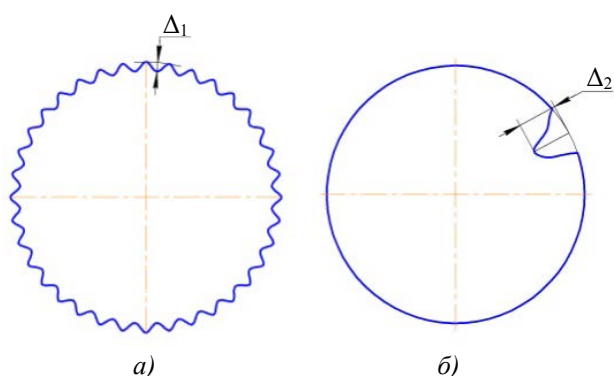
Профиль поперечного сечения цилиндрической поверхности детали:
